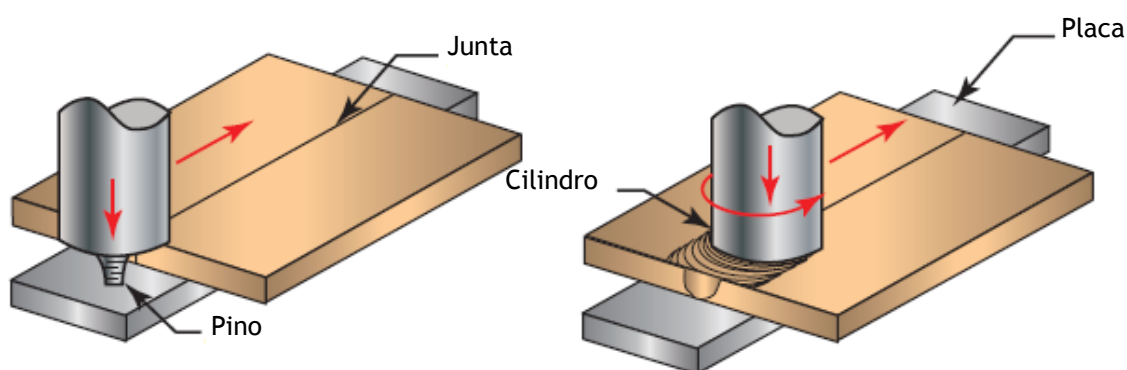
Princípio de funcionamento da soldadura Friction Stir Welding (FSW)
